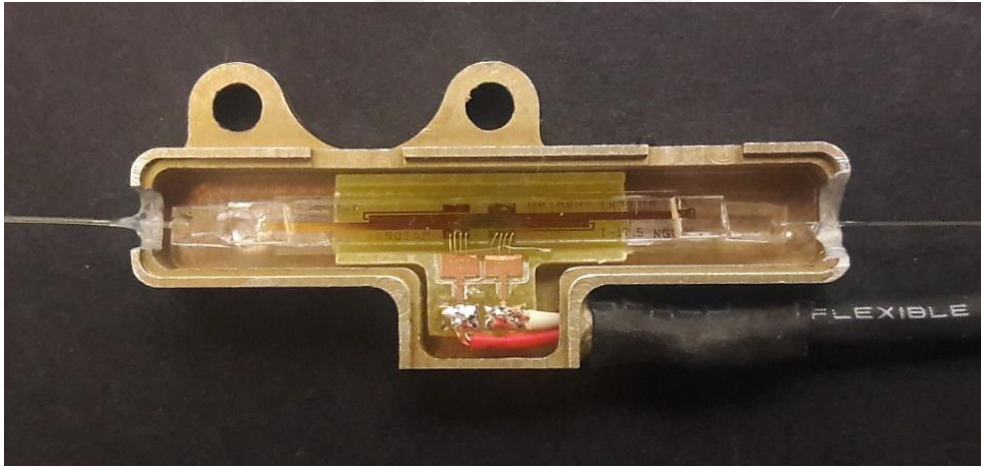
Entegre optik aygıt elektrotları ve PCB taşıyıcı üzerindeki bakır yüzeyler arasında elektriksel tel ile bağlantı yapılması
